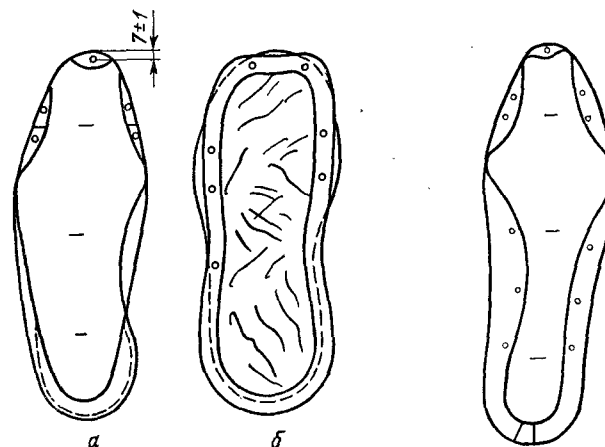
Схема обтяжки заготовки верха обуви со свободной затяжной кромкой (а) и с пристроченным рантом (б)
